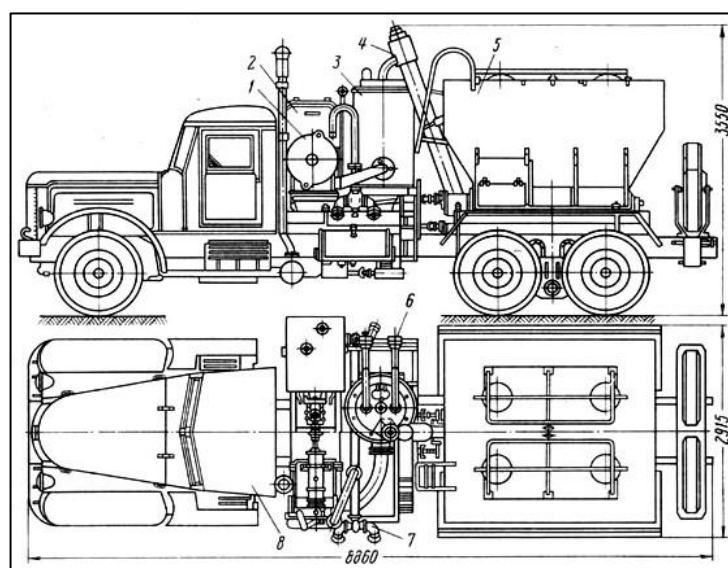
Пескосмесительный агрегат ЗПА: 1 - центробежный насос 4ПС; 2 - силовой блок двигателя ГАЗ-51; 3 - смесительное устройство; 4 - наклонный шнек; 5 - бункер для песка; 6 - приемный трубопровод; 7 - раздаточный трубопровод; 8 - автомобиль КраЗ-257
